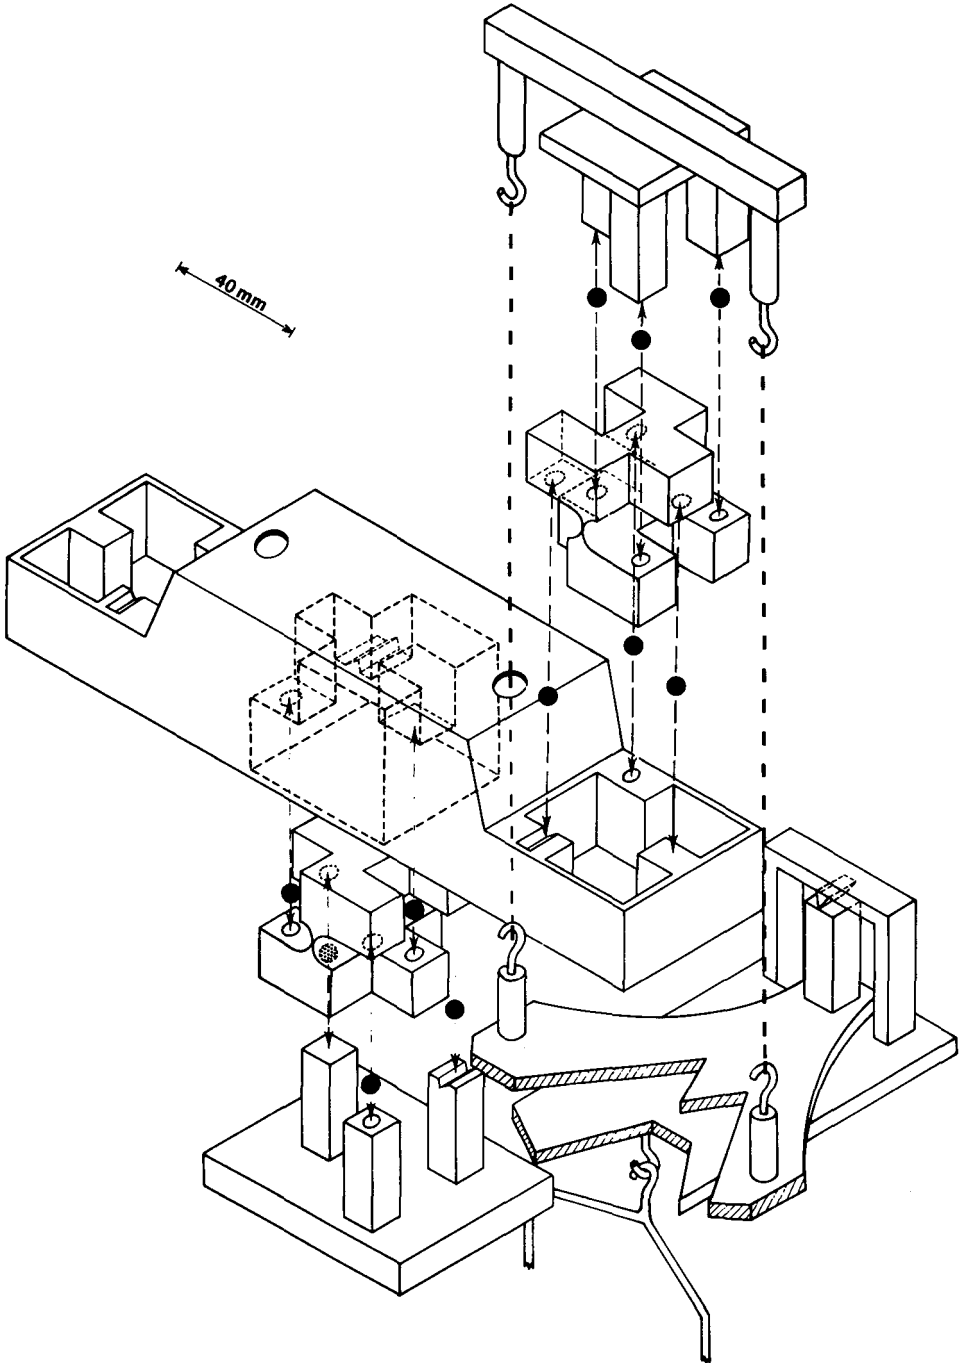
Vue éclatée d'ensemble d'un modèle de balance comportant des suspensions flexibles.
